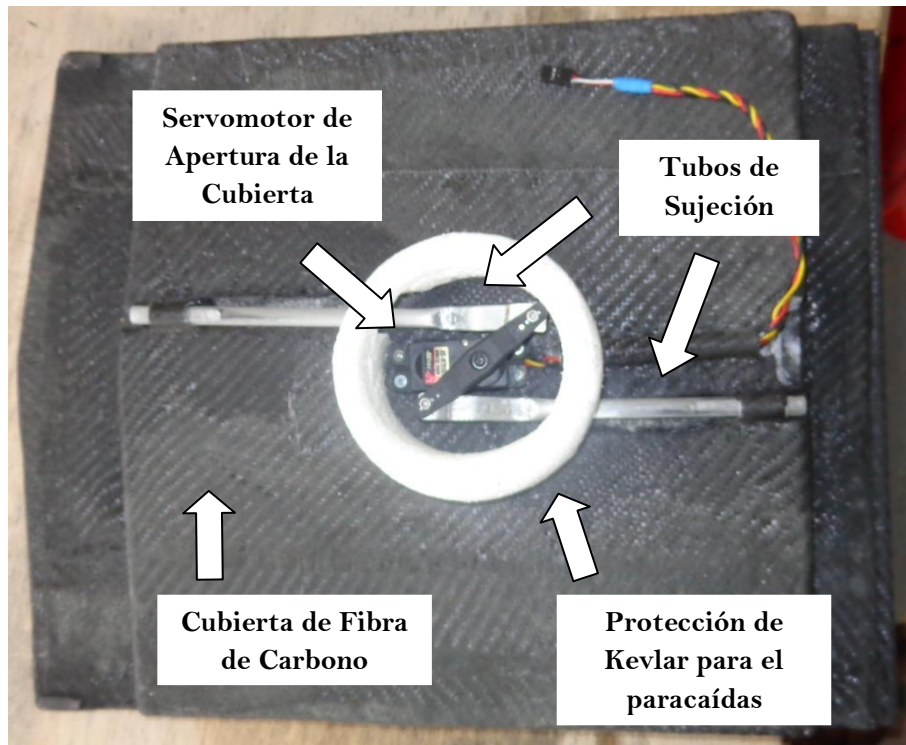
Instalación del Sistema Mecánico Ensamblado
